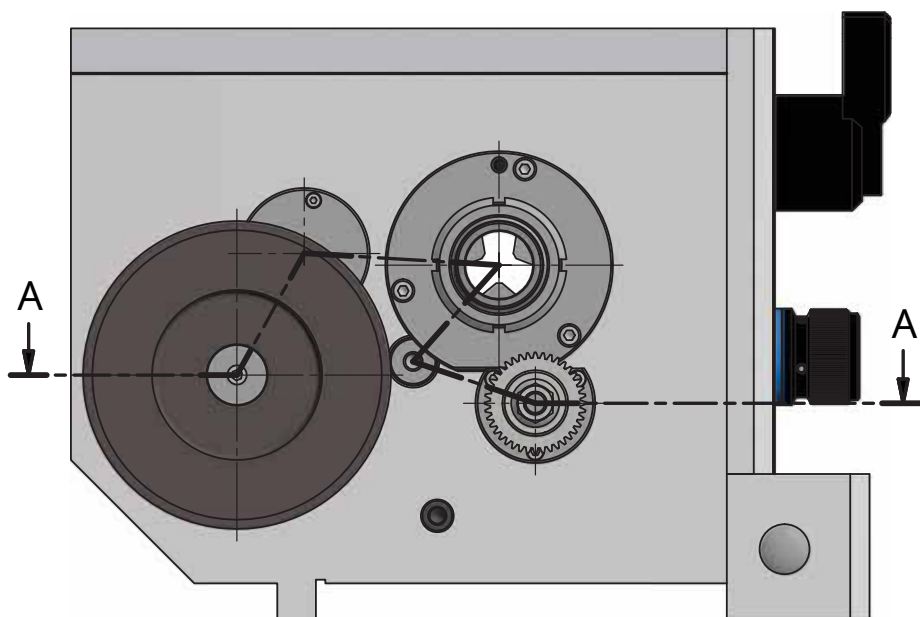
Getriebe Spindelstock 1-6 - Engranaje del cabezal 1-6
